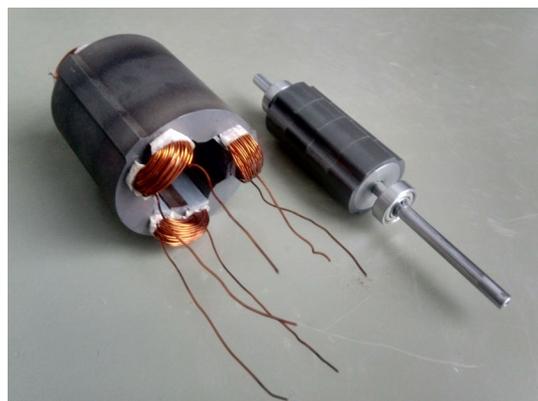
Stator mit Zahnspulenwicklungen (links) und Rotor mit Ringmagneten (rechts)
